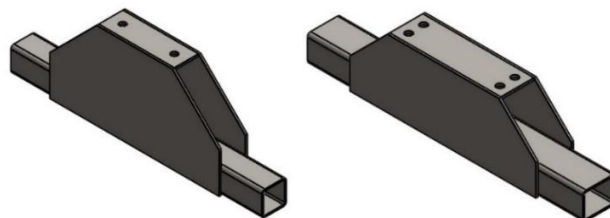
Soporte unidades de rodamiento y freno dinamométrico
